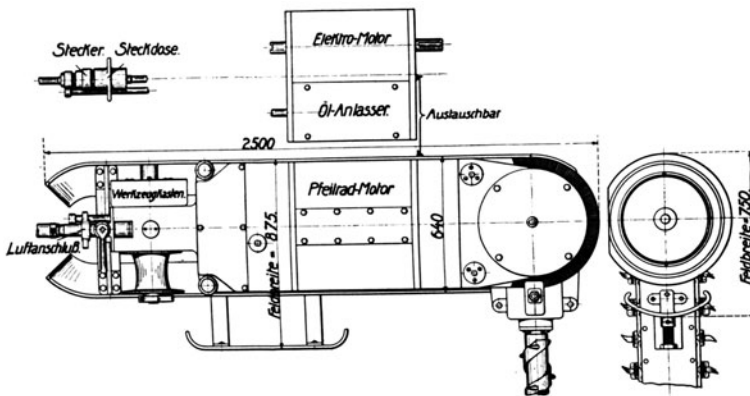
Schrämmaschine mit austauschbarem Motor und Schrämkopf.
